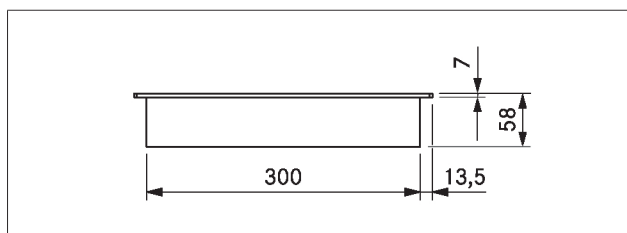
CKI apparatets dimensjoner sett forfra
